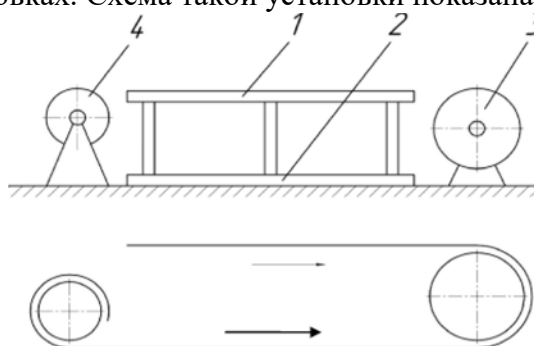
Схема двухъярусного станка: а — схема станка; б — схема движения полотнища
